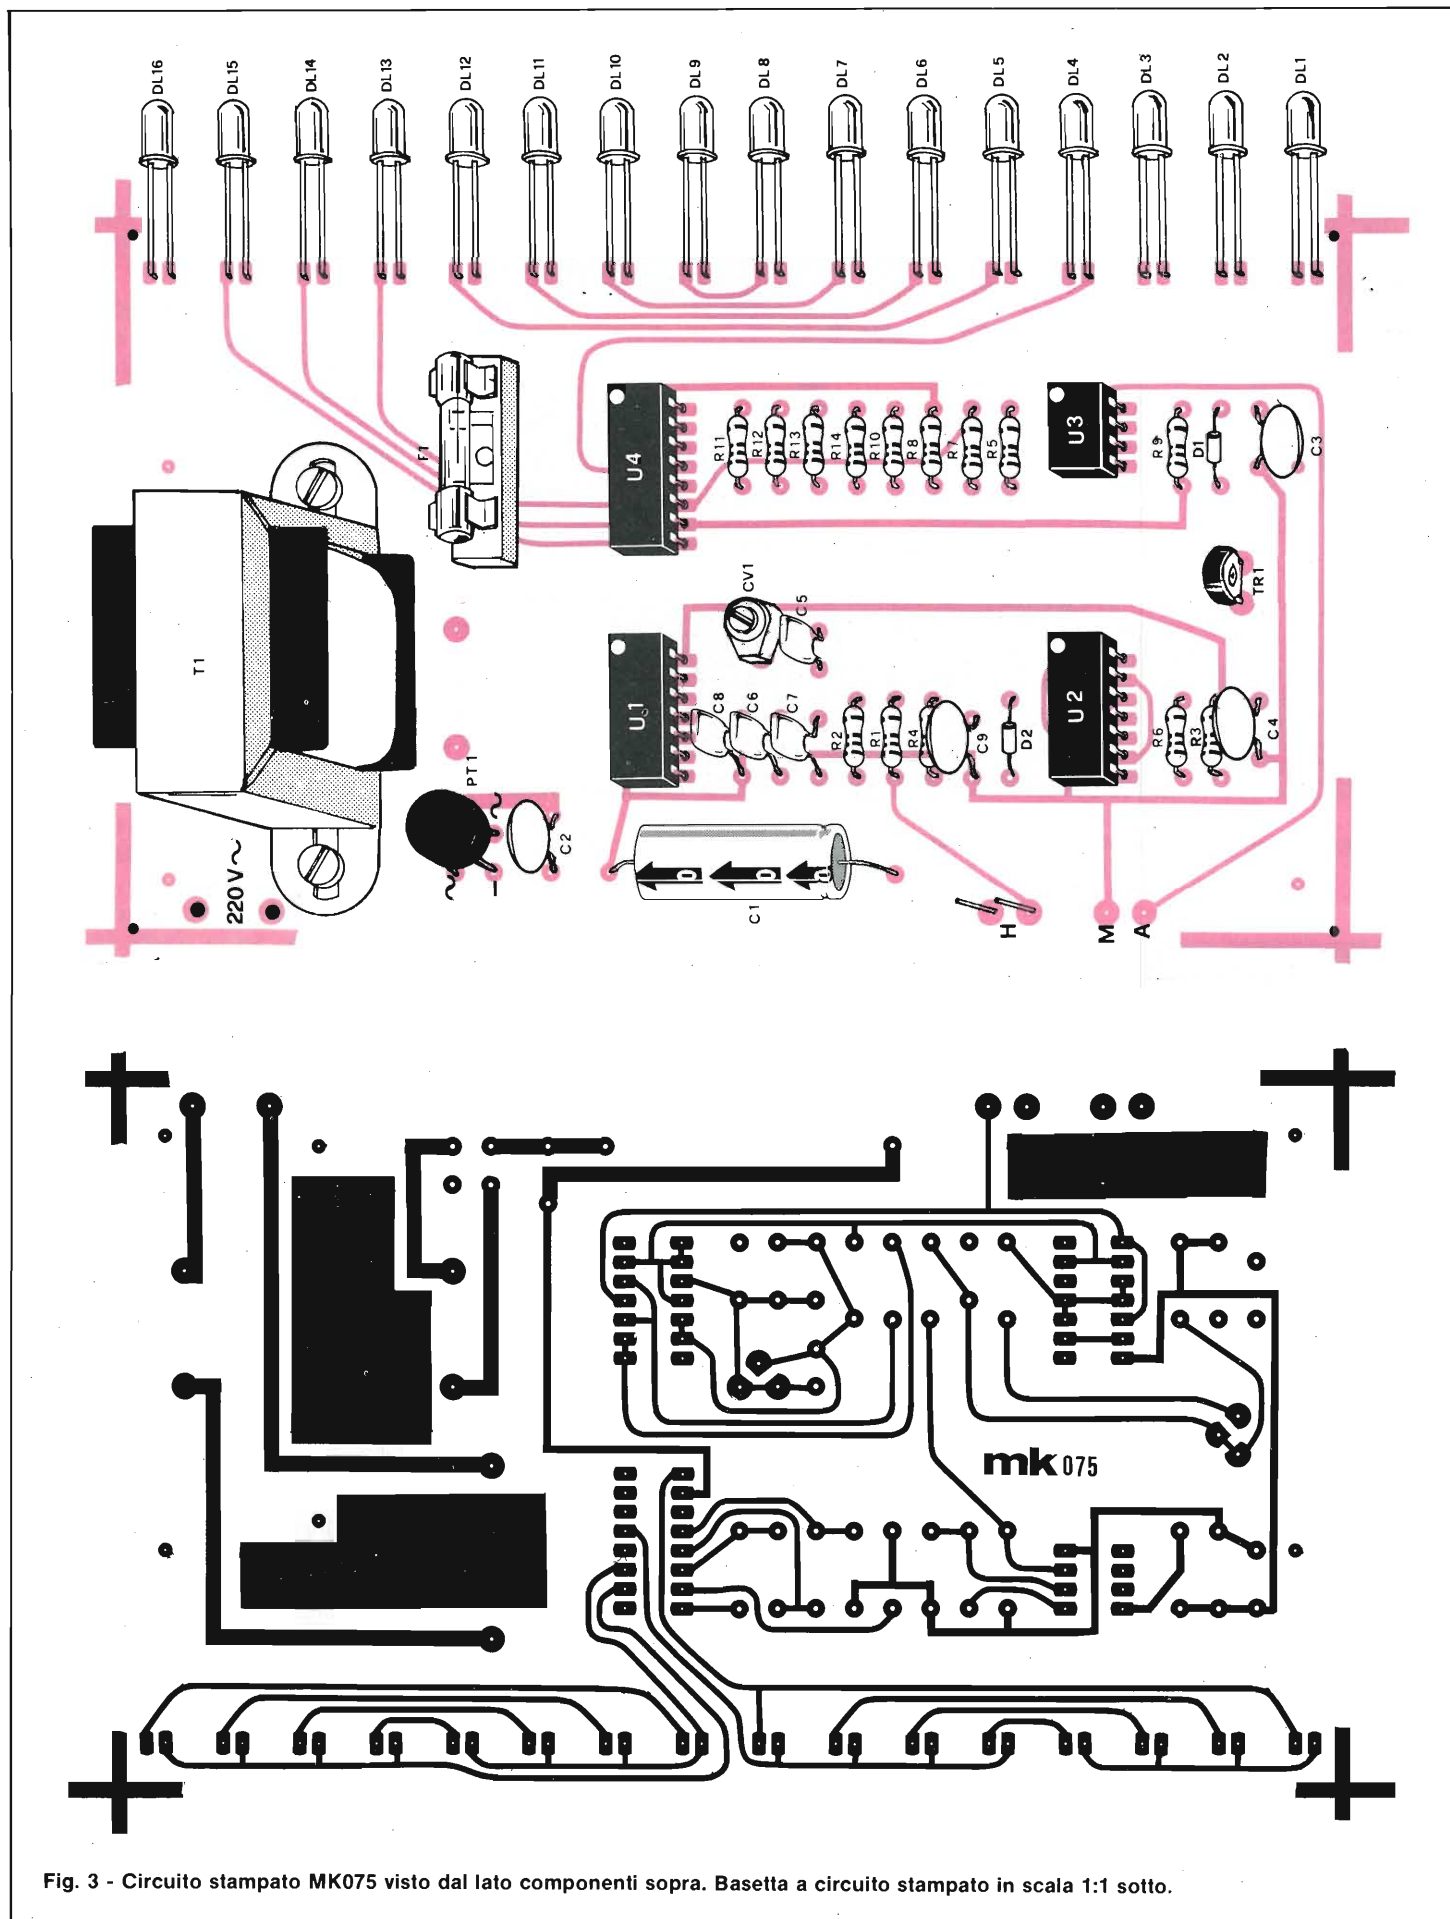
Circuito stampato MK075 visto dal lato componenti sopra. Basetta a circuito stampato in scala 1:1 sotto.
